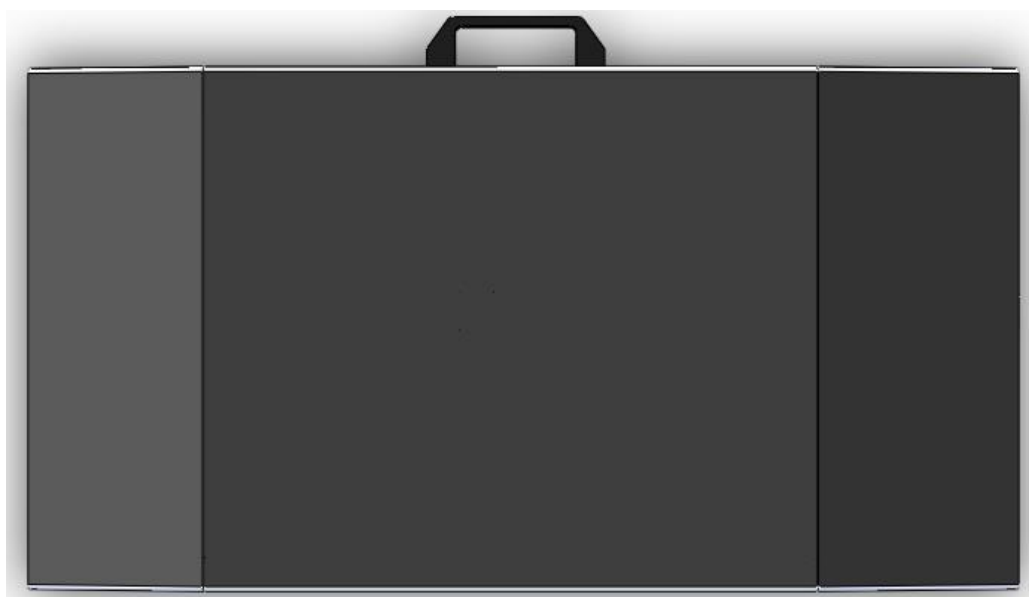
Rampa portátil em posição fechada de maleta de mão. Fonte: elaborado pelos autores.
